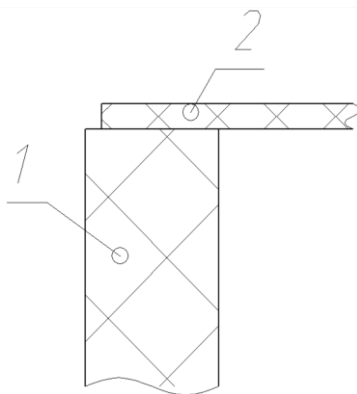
Наложение задней стенки в нахлест. 1 – Боковая стенка изделия. 2 – Задняя стенка изделия.
